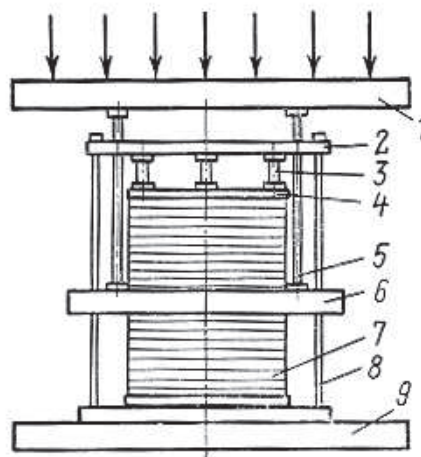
Схема установки обмотки в прессующих устройствах: 1 — верхняя плита пресса; 2 — прессующие плиты обмотки; 3 — тензометрические стойки; 4 — прессующие кольца; 5 — дополнительные стойки; 6 — средняя плита; 7 — обмотка; 8 — нижняя плита пресса; 9 — шпилька для начальной запрессовки
